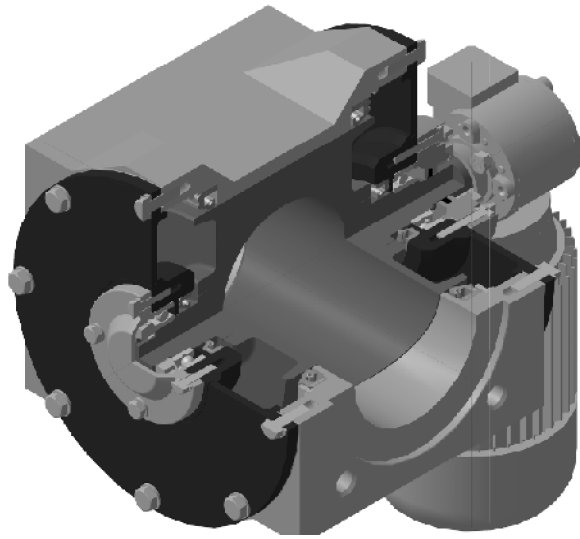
Клапан-пульсатор для циклической подачи газа в аппараты с беспровальными перфорированными решетками
